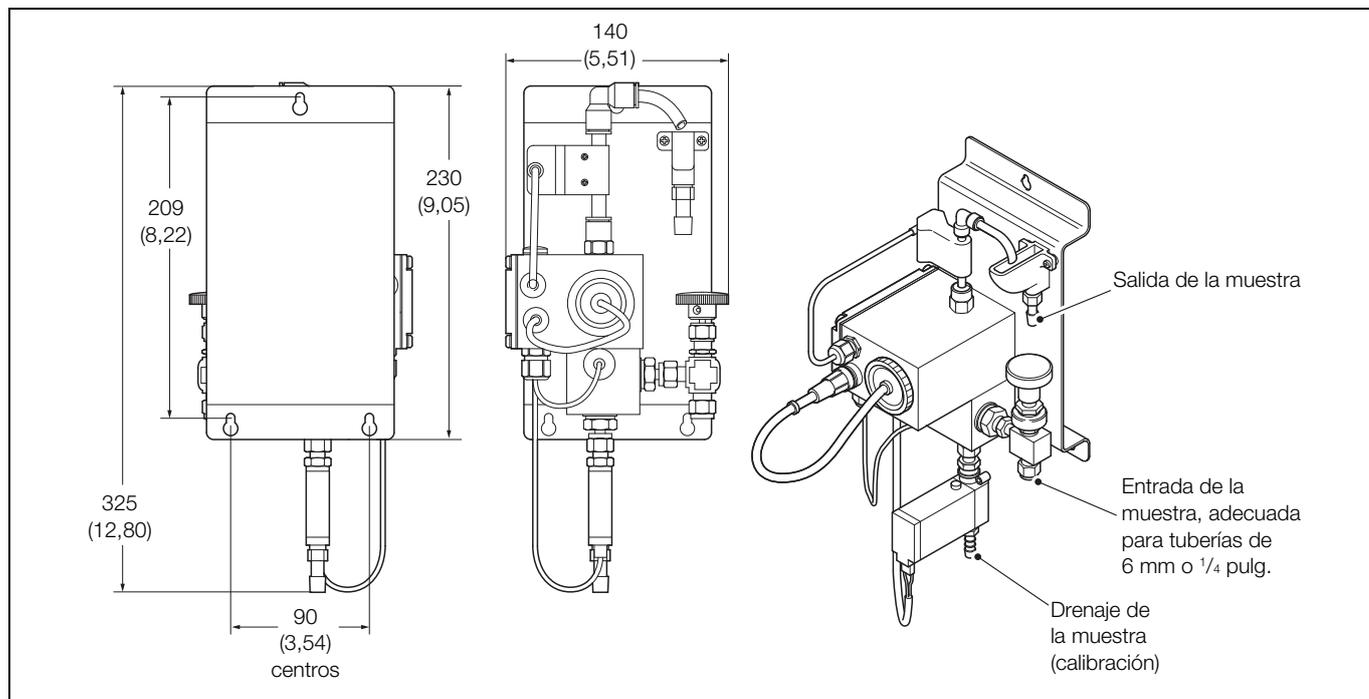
Dimensiones de la sección de medición ADS551/panel de montaje
